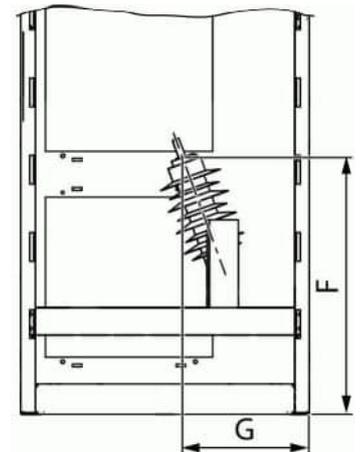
Vista frontale (scaricatore di sovratensione a destra)
